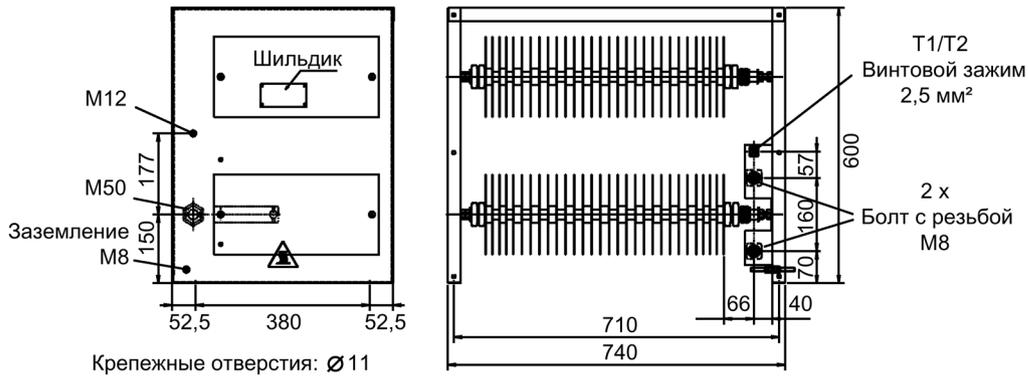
Габаритный чертеж тормозного резистора 25 кВт
